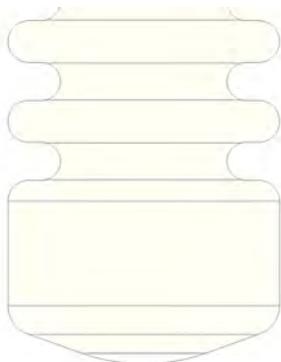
Sistema "con junta del asiento de la válvula integrada"
